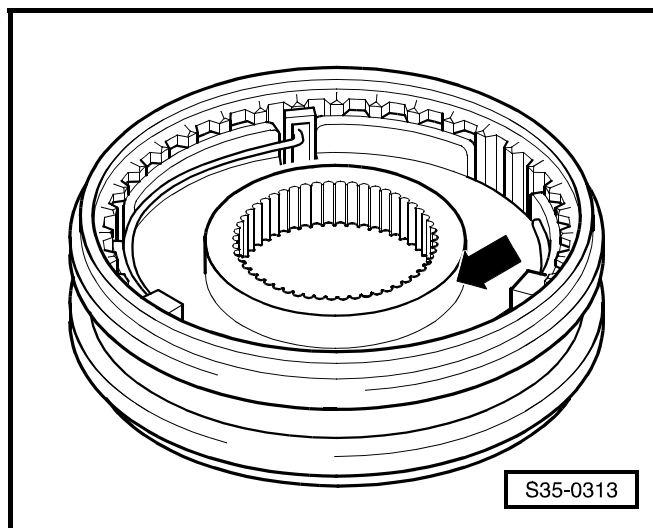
Запрессовывание каретки синхронизатора со скользящей муфтой для 3-ей и 4-ой передач
